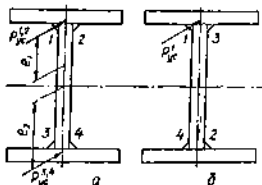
Технологические варианты изготовления сварной двутавровой балки
